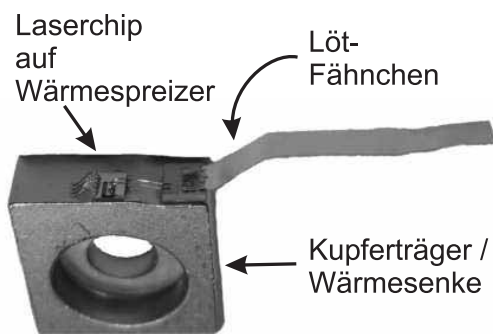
Laserdiode, die von OSRAM auf einen C-Mount montiert wurde. Die Bohrung dient der Befestigung mit einer M2-Schraube.
